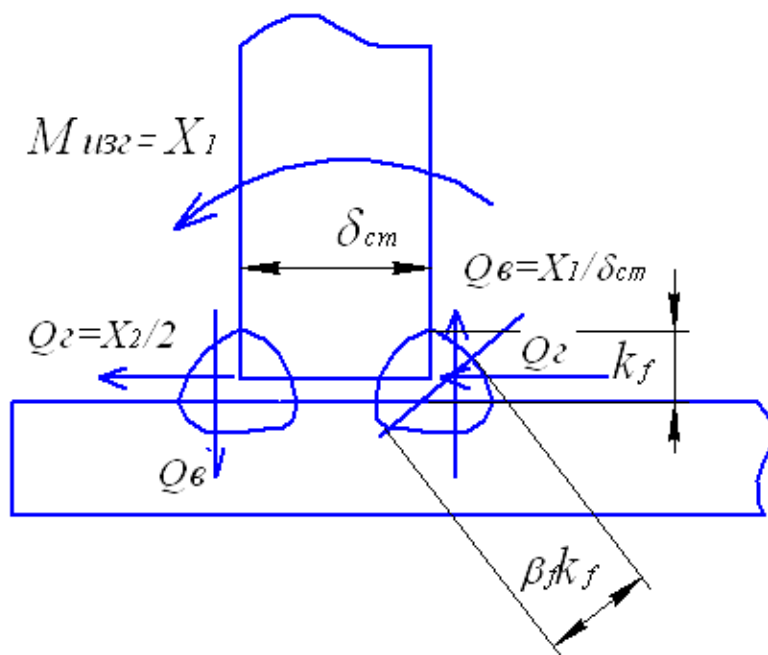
Расчетная схема для расчета сварного шва
